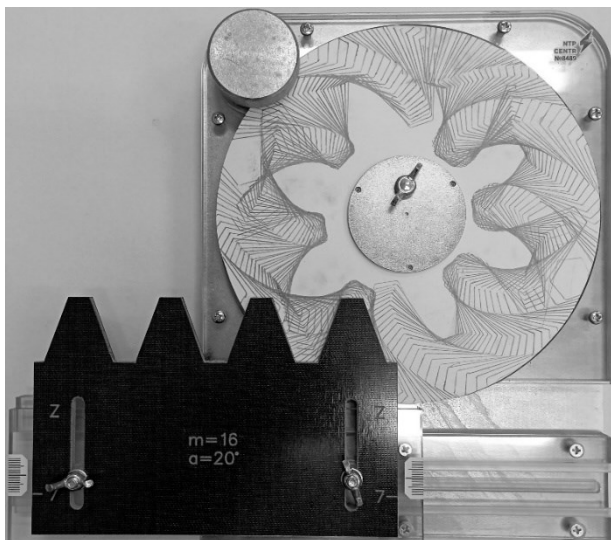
Процесс нарезания зубчатого колеса со смещением инструмента
